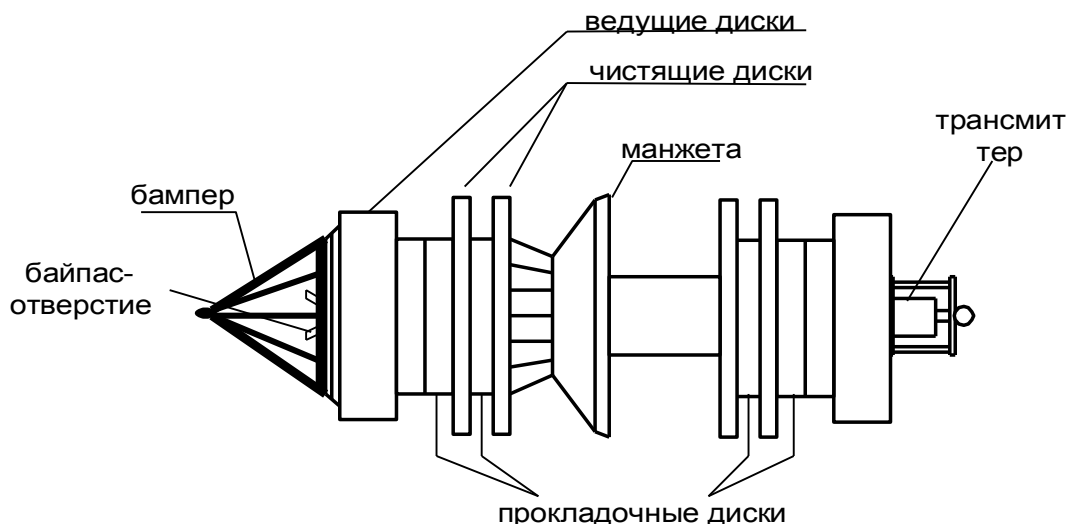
Внешний вид очистного скребка
